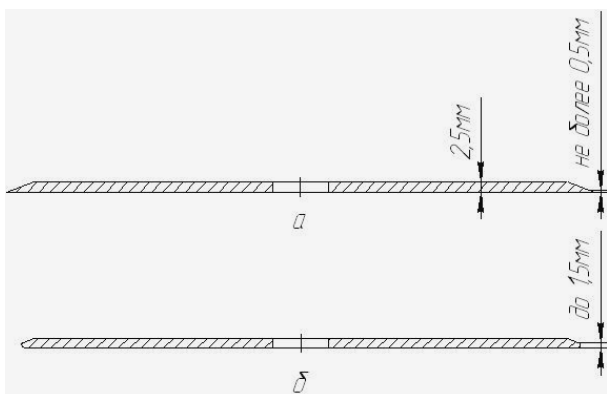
Поперечное сечение детали типа диск: а – исходная форма поперечного сечения детали; б – форма поперечного сечения детали после износа
